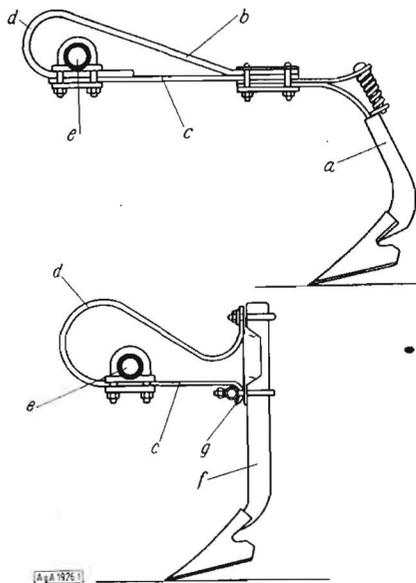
Werkzeughalter für Bodenbearbeitungsgeräte
